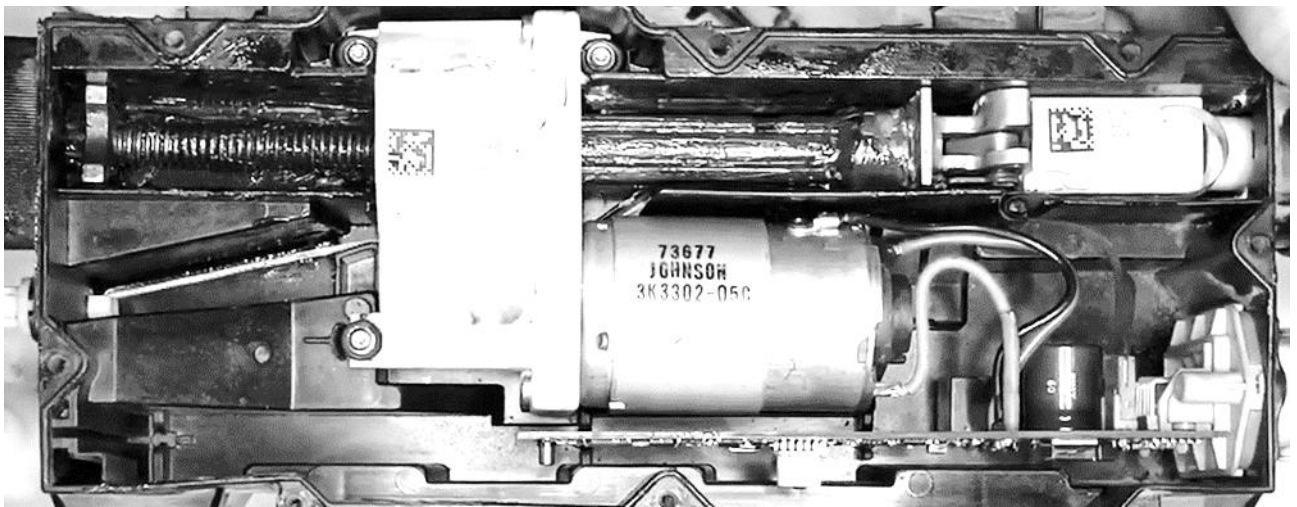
Загальна компоновка блоку стяжного приводу EPB
